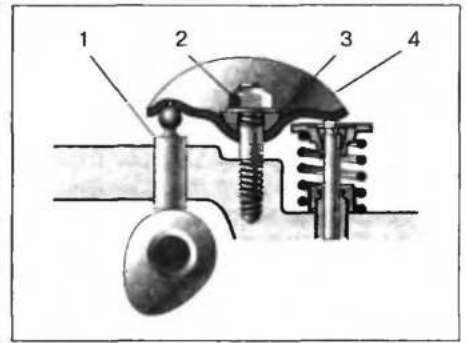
Цилиндрический толкатель в схеме привода клапана коромыслом: 1 — толкатель; 2 — гайка с тугой резьбой; 3 — сферическая опора; 4 — коромысло
